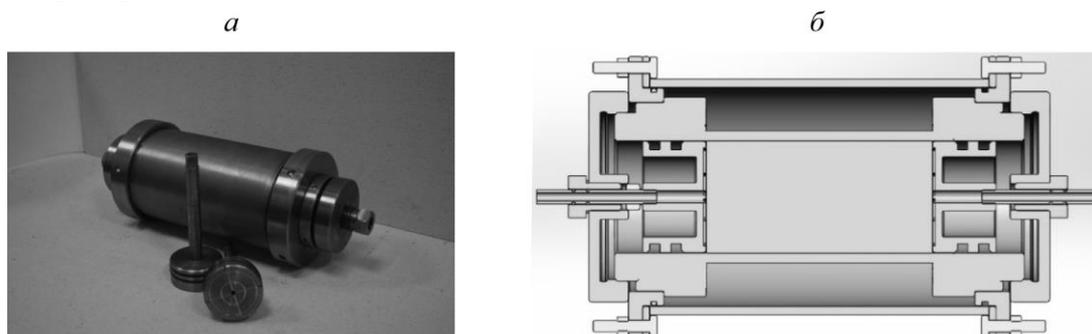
Камера высокого давления: а — внешний вид; б — внутренний вид
